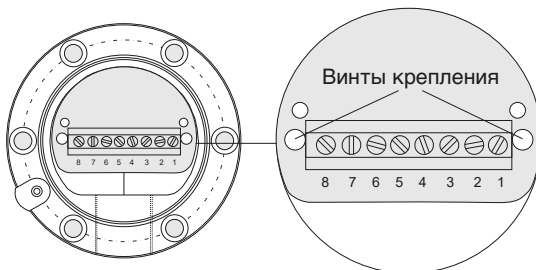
Типовой корпус с узлом соединительной клеммы, распределение контактов
